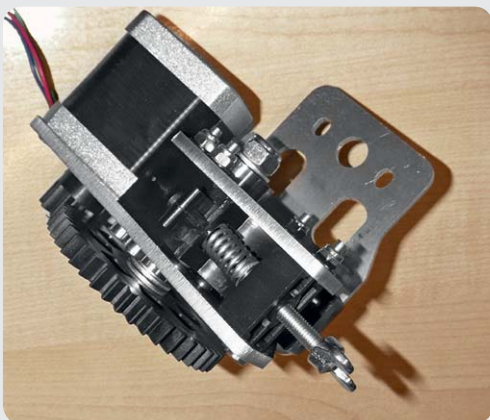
Fertig aufgebaute Extruder-Baugruppe ...
